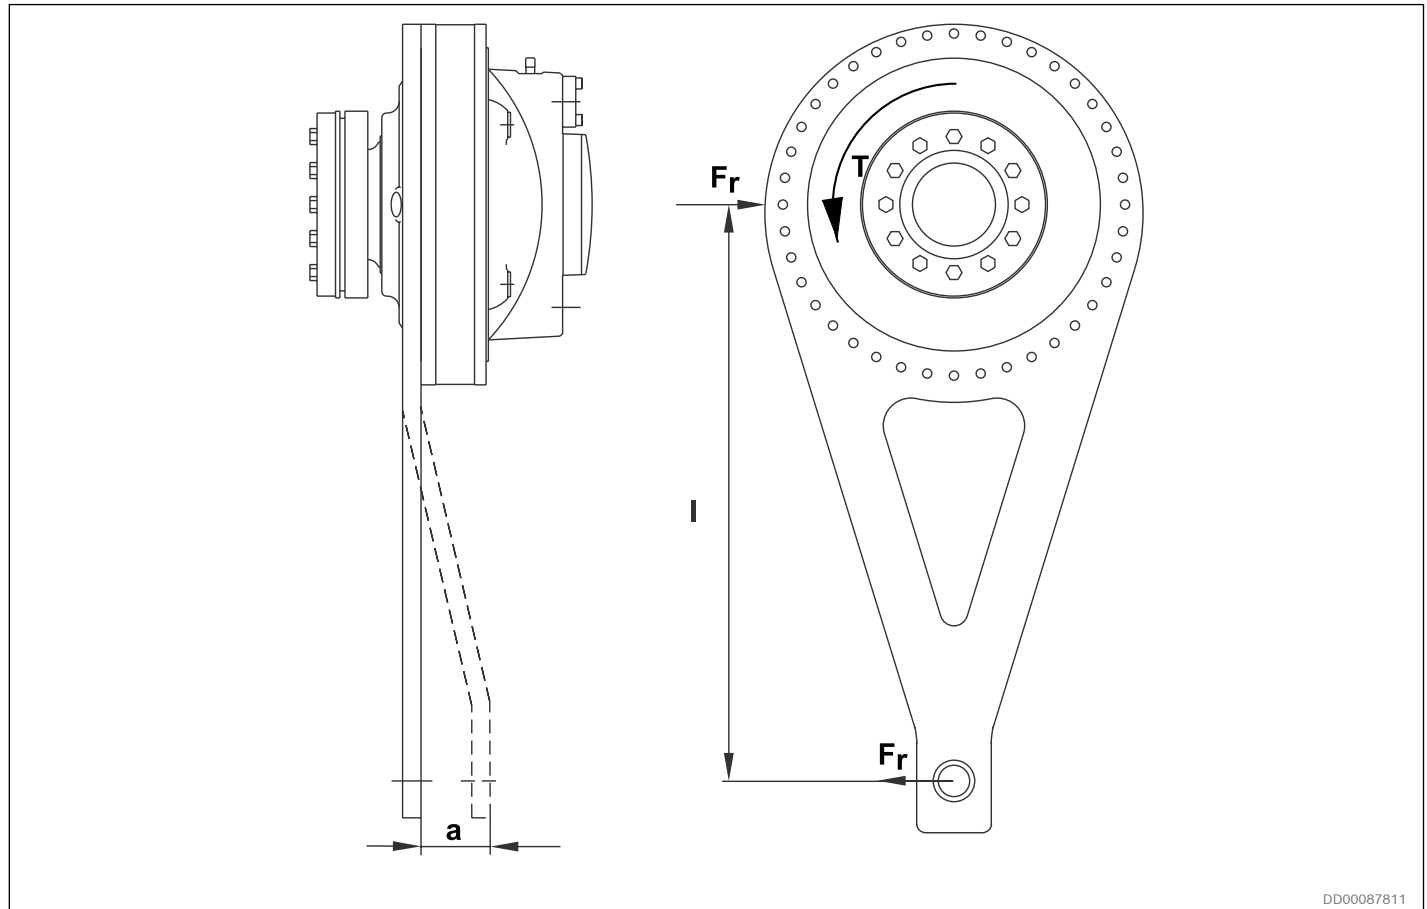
Motor instalado sobre el eje con brazo de torque.
